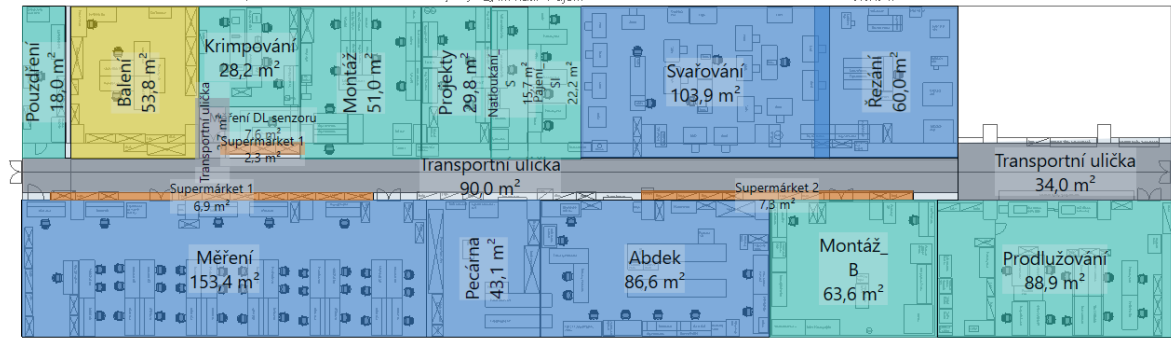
M2 layout 3. NP + M2 Layout přízemí (vlastní zpracování)
